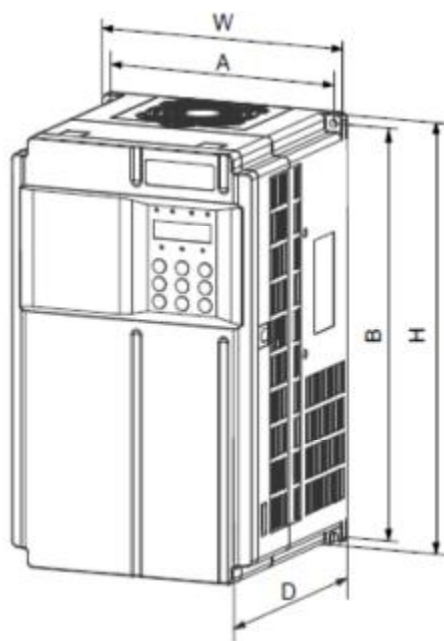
Внешний вид и монтажные размеры MD290 (металлический корпус)
